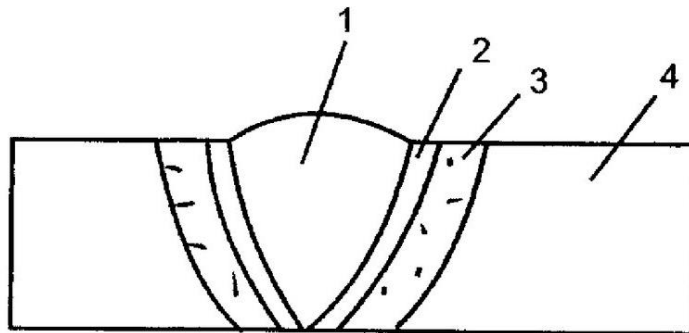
Схема будови структури металу зварних швів: 1- зварний шов, 2 – зона сплавлення, 3 – зона термічного впливу (ЗТВ) зварювання, 4 – основний метал.
